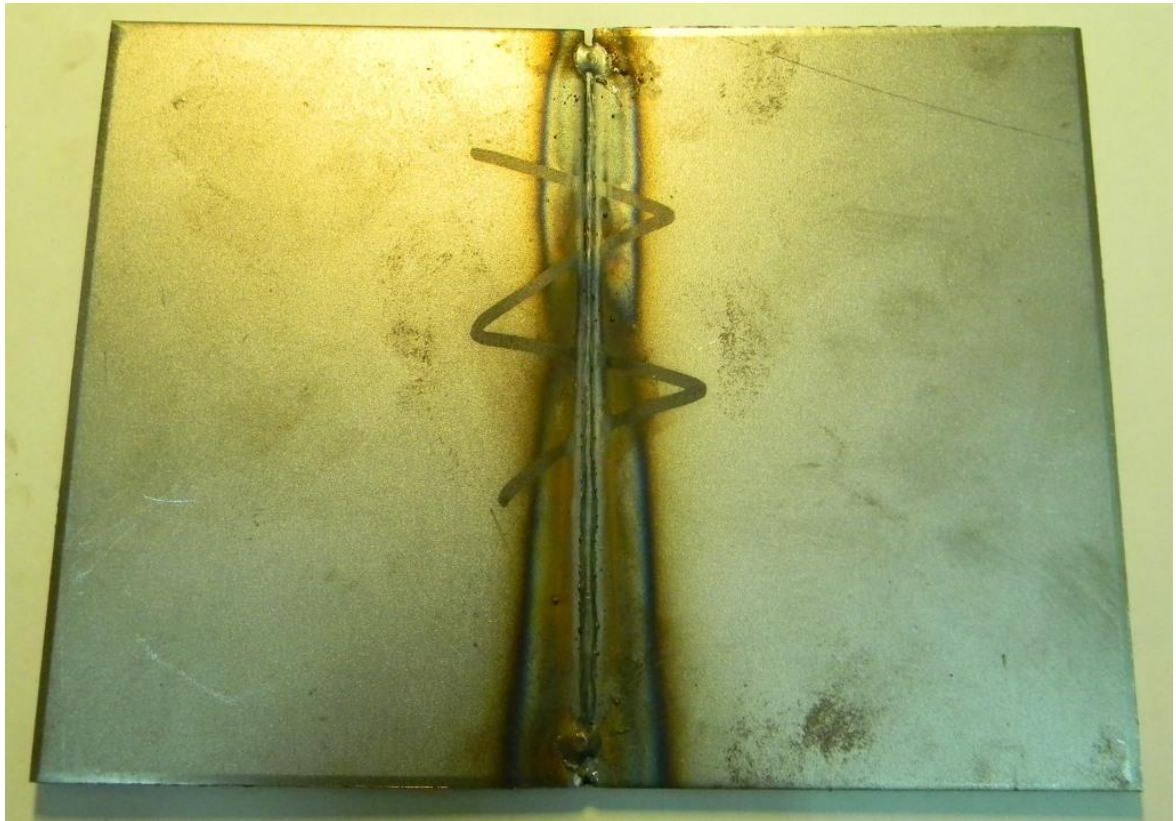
Образец после сварки подготовленный вырубкой с EPS
